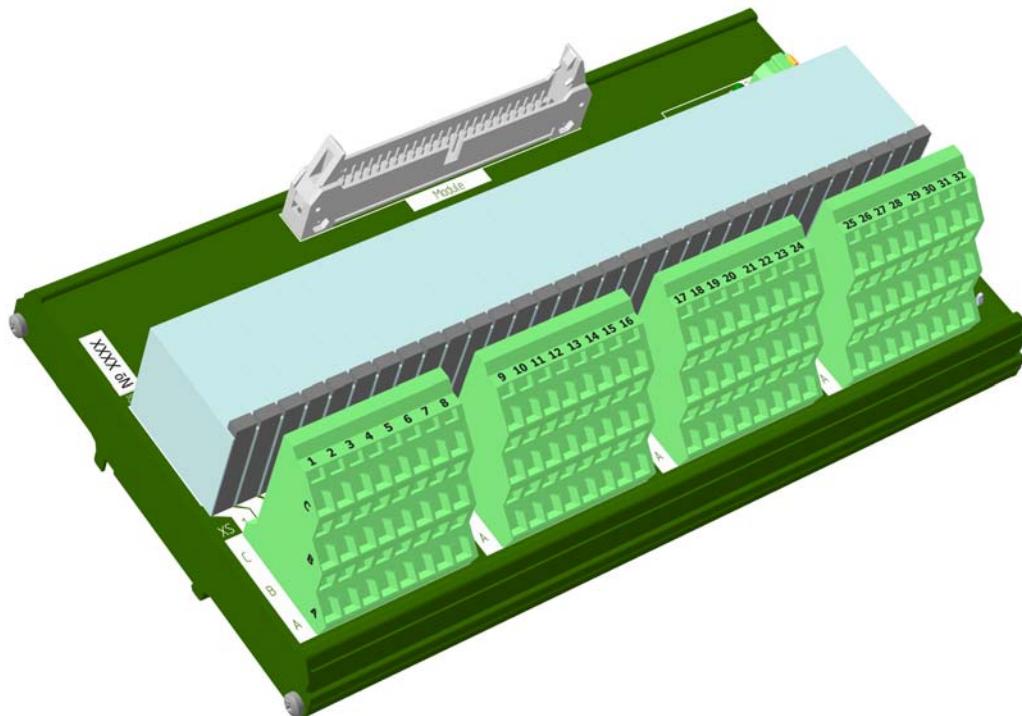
Чертеж общего вида ТР-2О с указанием габаритных размеров
